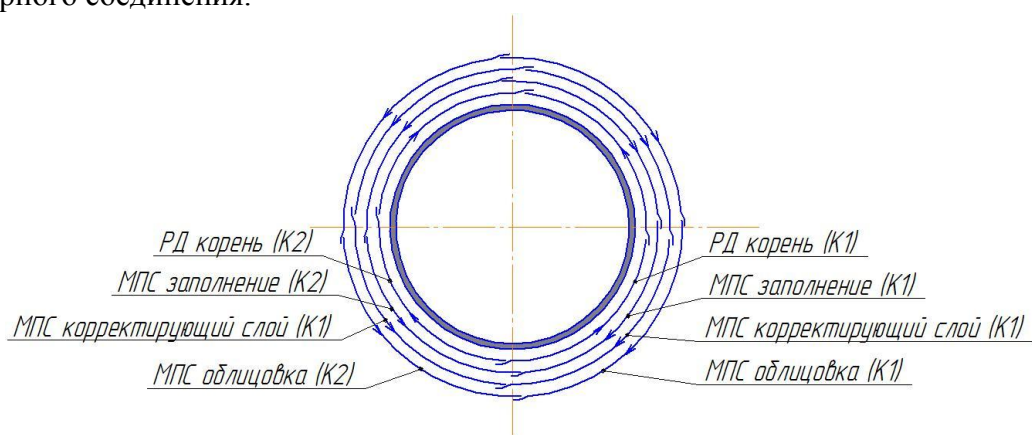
Последовательность сварки кольцевого стыка комбинированной сваркой РД+МПС. K1 и K2 – клейма сварщиков.
